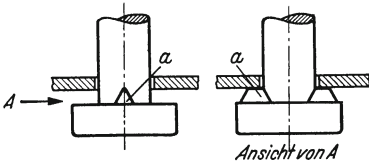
Gepreßte Buckel für Schmiedeteile, z. B. Einschweißen von Bolzen in Bleche. a = Buckel, beim Gesenkschmieden des Kopfes hergestellt.
